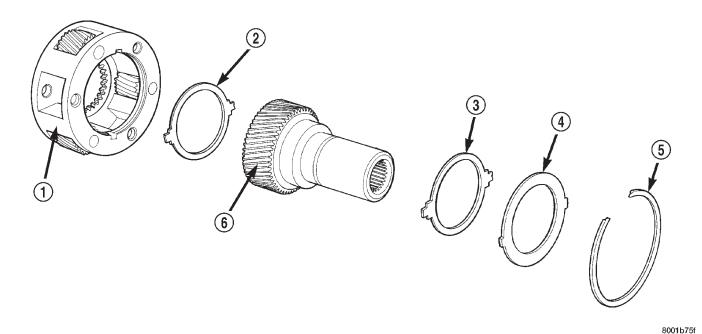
Componentes del engranaje impulsor y caja de satélites
